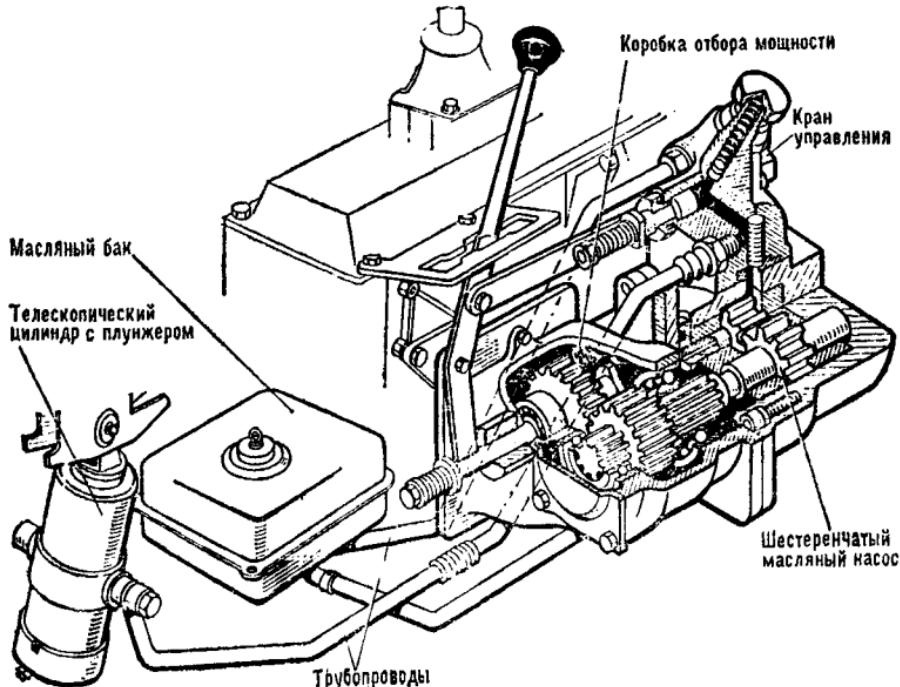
Подъемный механизм кузова автомобиля-самосвала
